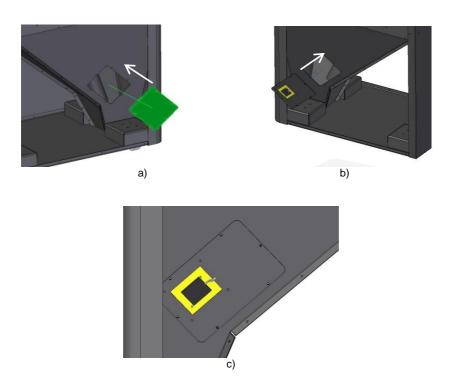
Colocação do sensor de nível de pellets no silo (instalação do silo à esquerda da caldeira)
